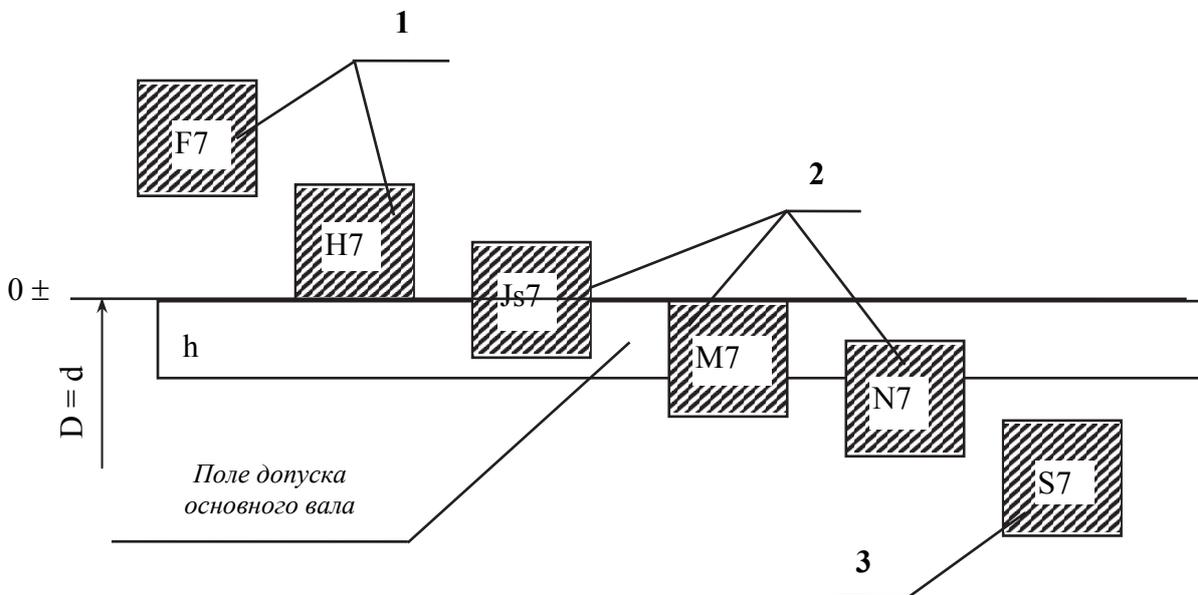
Расположение полей допусков отверстий и валов в системе вала:
